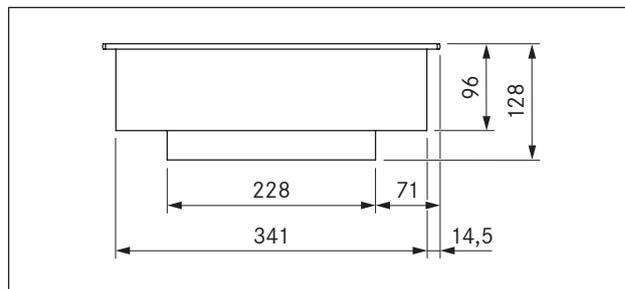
PKIW1 dimensões do aparelho vista frontal
